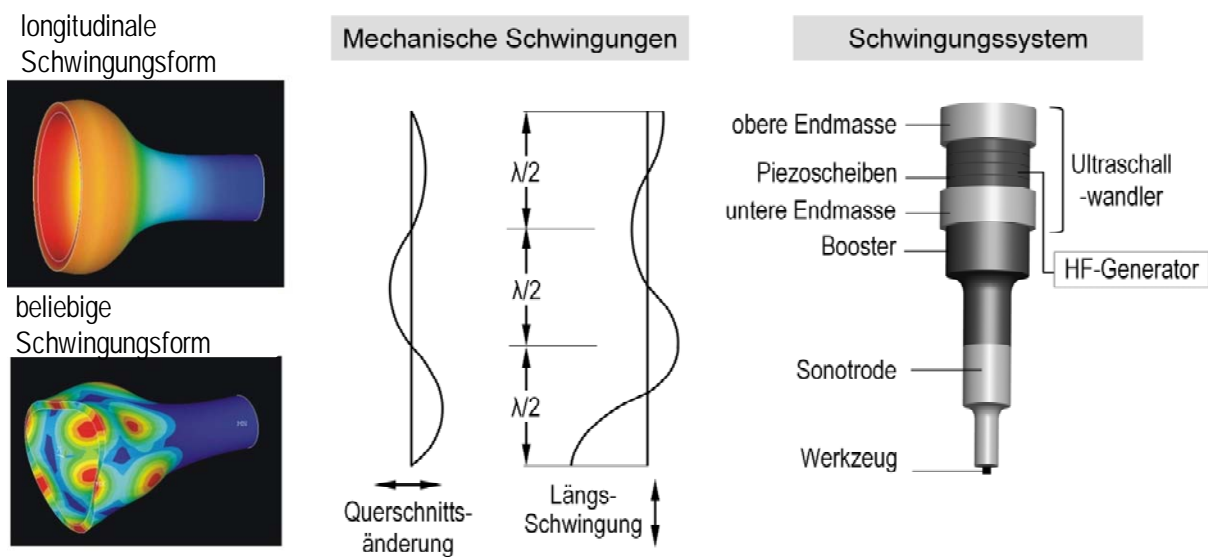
Schwingungskette – Ausbildung einer stehenden Ultraschallwelle und ausgewählte Schwingungsformen eingesetzter Werkzeuge
